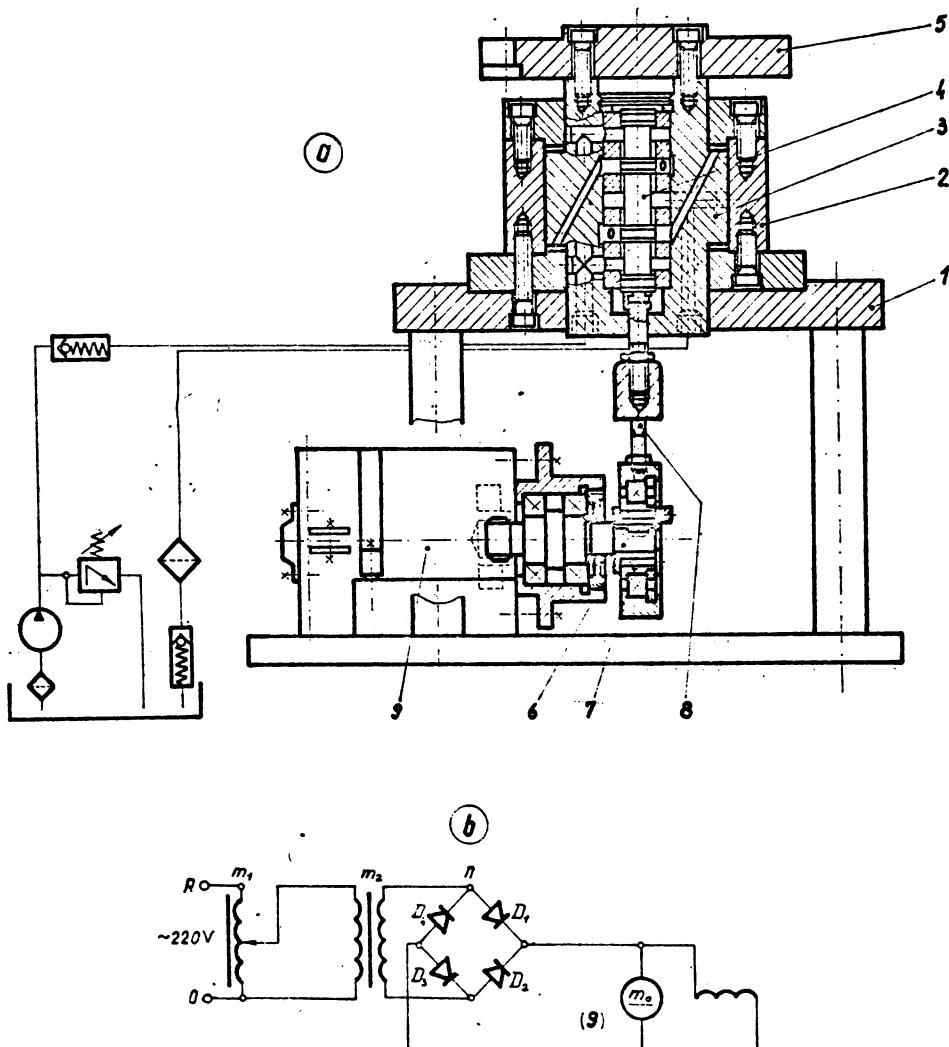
Schema constructivă de ansamblu a vibratorului hidraulic.
